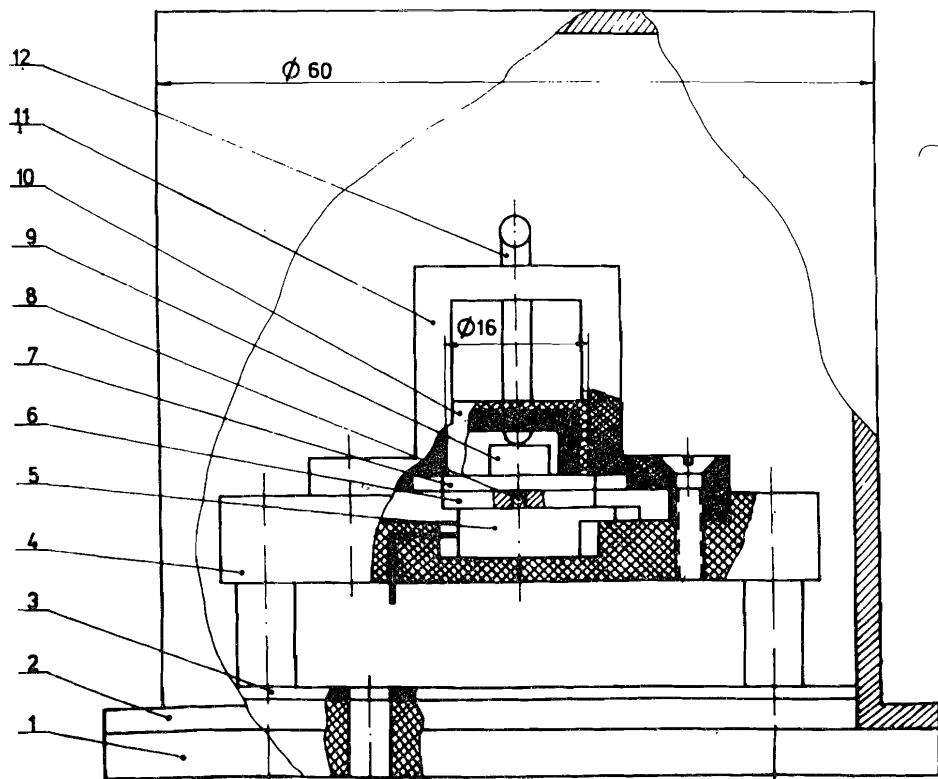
Конструкция микротермостата. 1 — основание кожуха, 2 — кожух, 3 — печатная плата, 4 — основание, 5 — транзистор-нагреватель, 6 — алюминиевая прокладка, 7 — изолирующая пластина, 8 — диод-датчик, 9 — испытуемый образец, 10 — тепловой экран, 11 — фланец, 12 — прижимное устройство.
